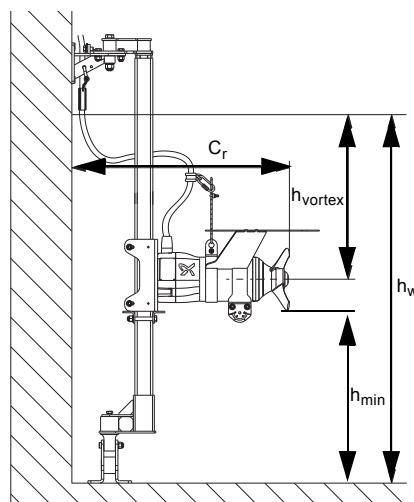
Схема монтажа на стойке мешалок с противовихревым экраном
